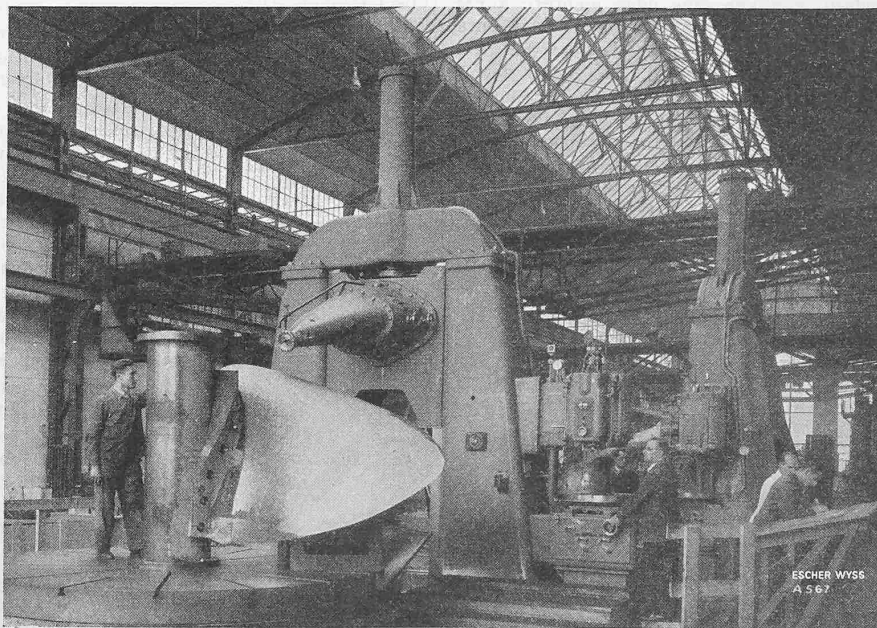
Kopierfräsmaschine für Schiffschrauben, Fräsprüfung im Werk
